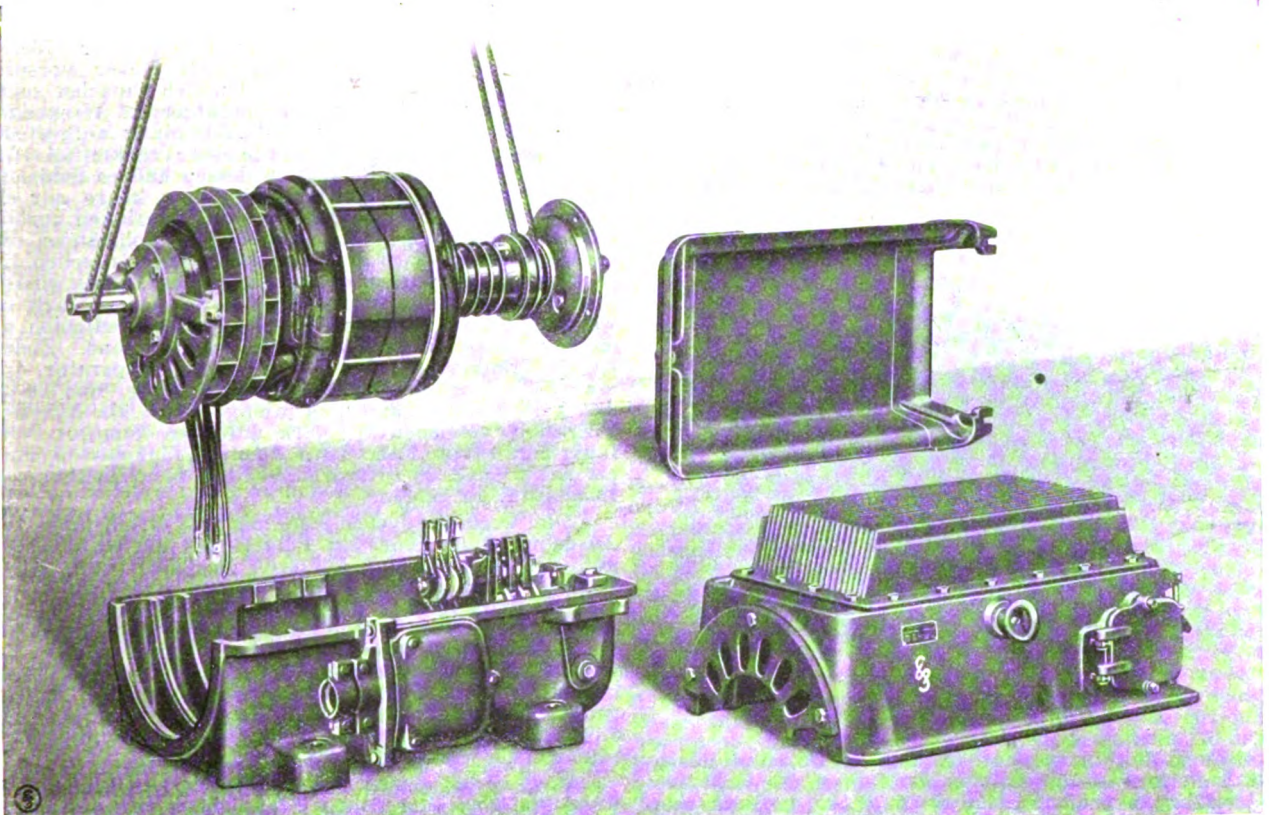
Einzelteile des Motors mit Umlauf-Rückkühlung.
